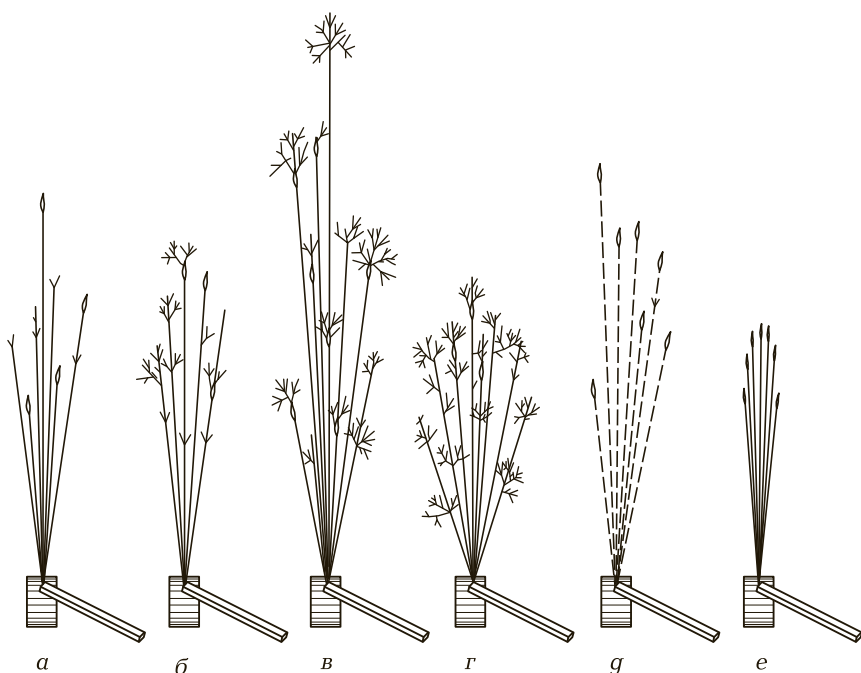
Формы пучка искр некоторых марок стали и твердого сплава, образующихся при шлифовании заготовок:
